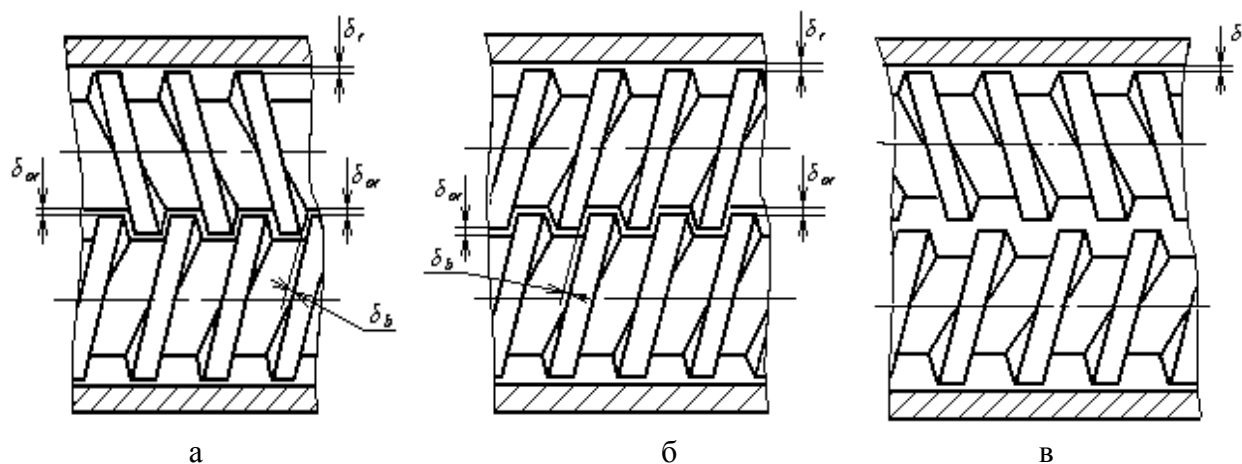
Типичная конструкция двухчервячного экструдера
